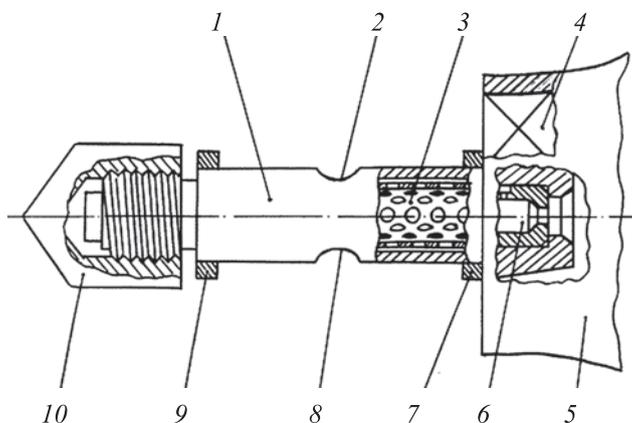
Штатная форсунка ГТД марки НК-8-2У
